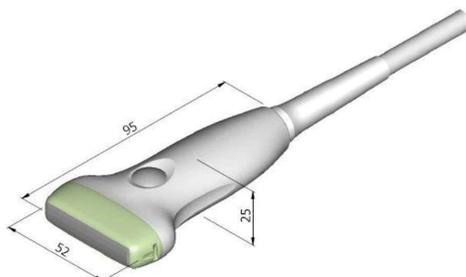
Disegno tecnico e dimensioni (mm)
